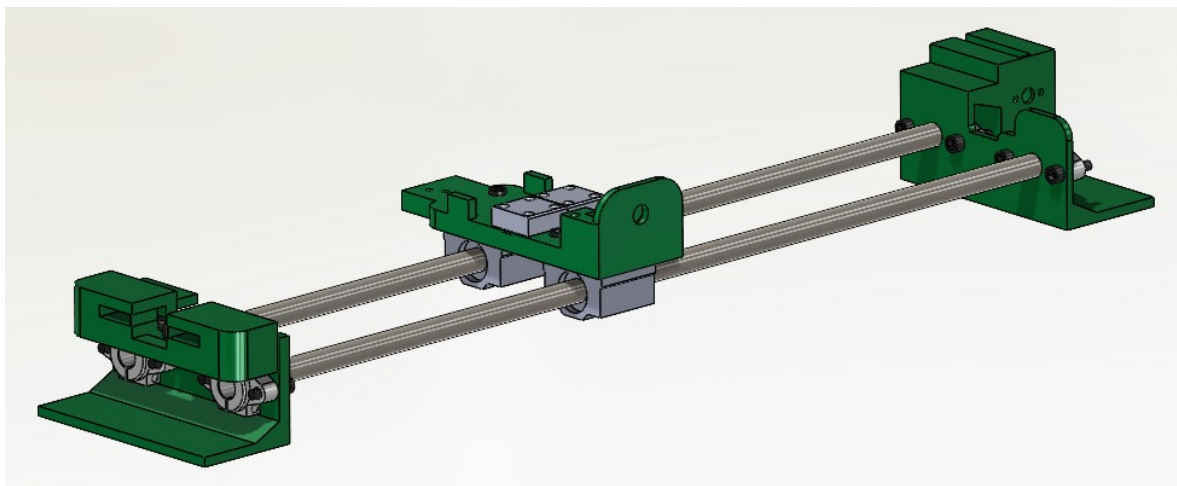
Ensamblaje del diseño mecánico de la planta
